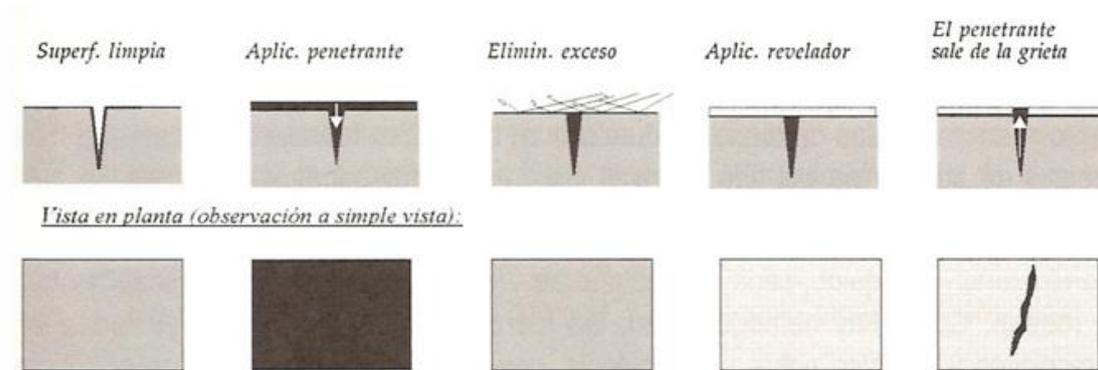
Fundamento del ensayo por líquidos penetrantes.
